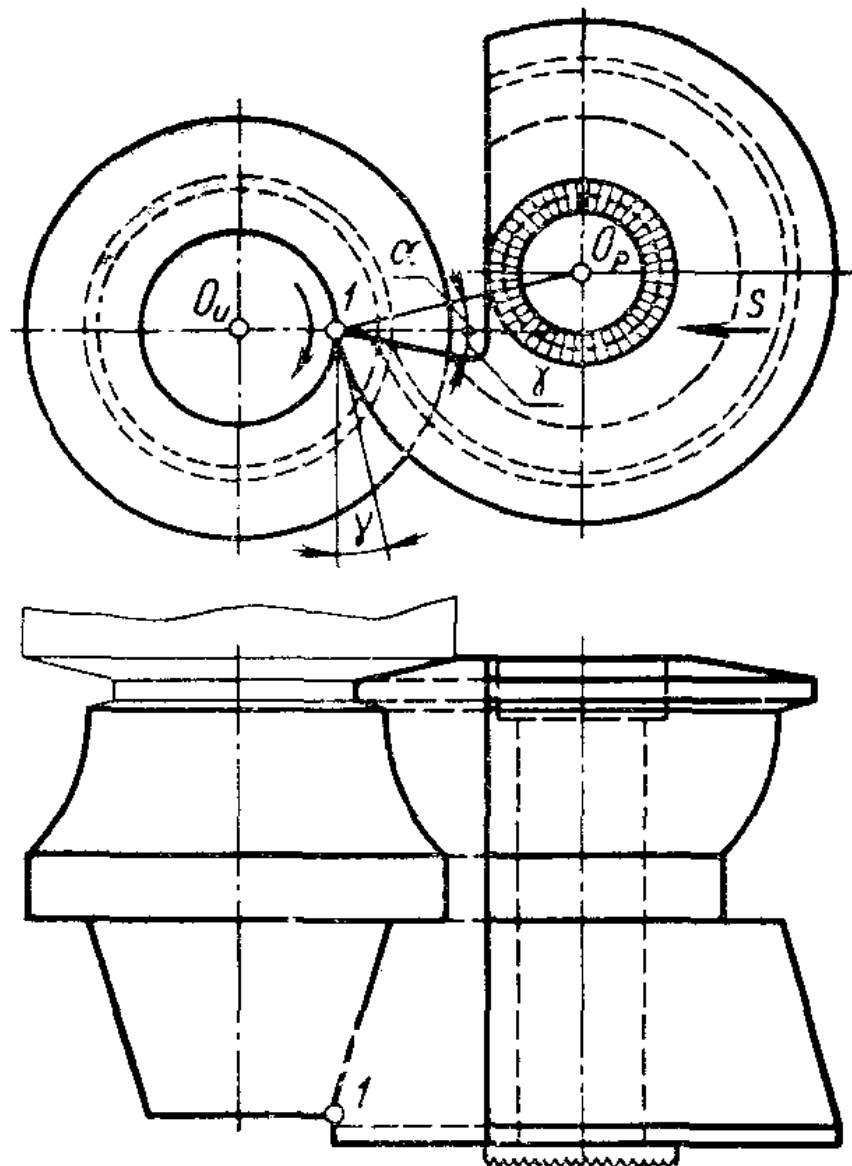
Круглий фасонний різець, встановлений базової точки 1 на висоті центру деталі
